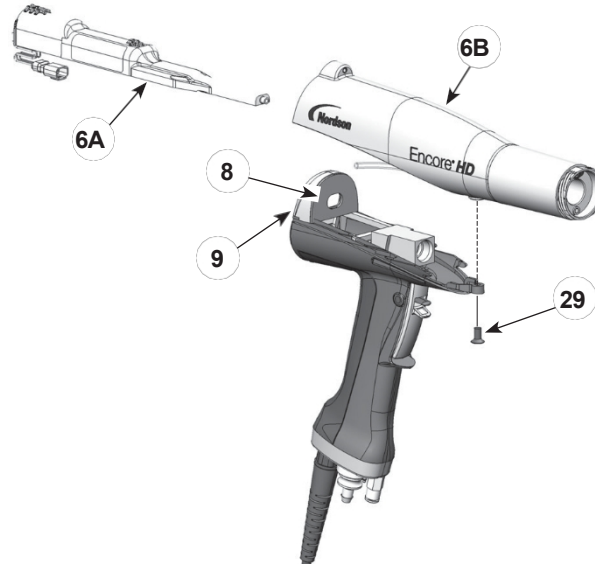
Entfernen des Netzteils aus dem Pistolengehäuse
